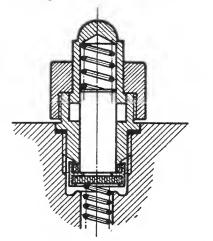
Nockenventil für Direktdruck mit Druckausgleich
